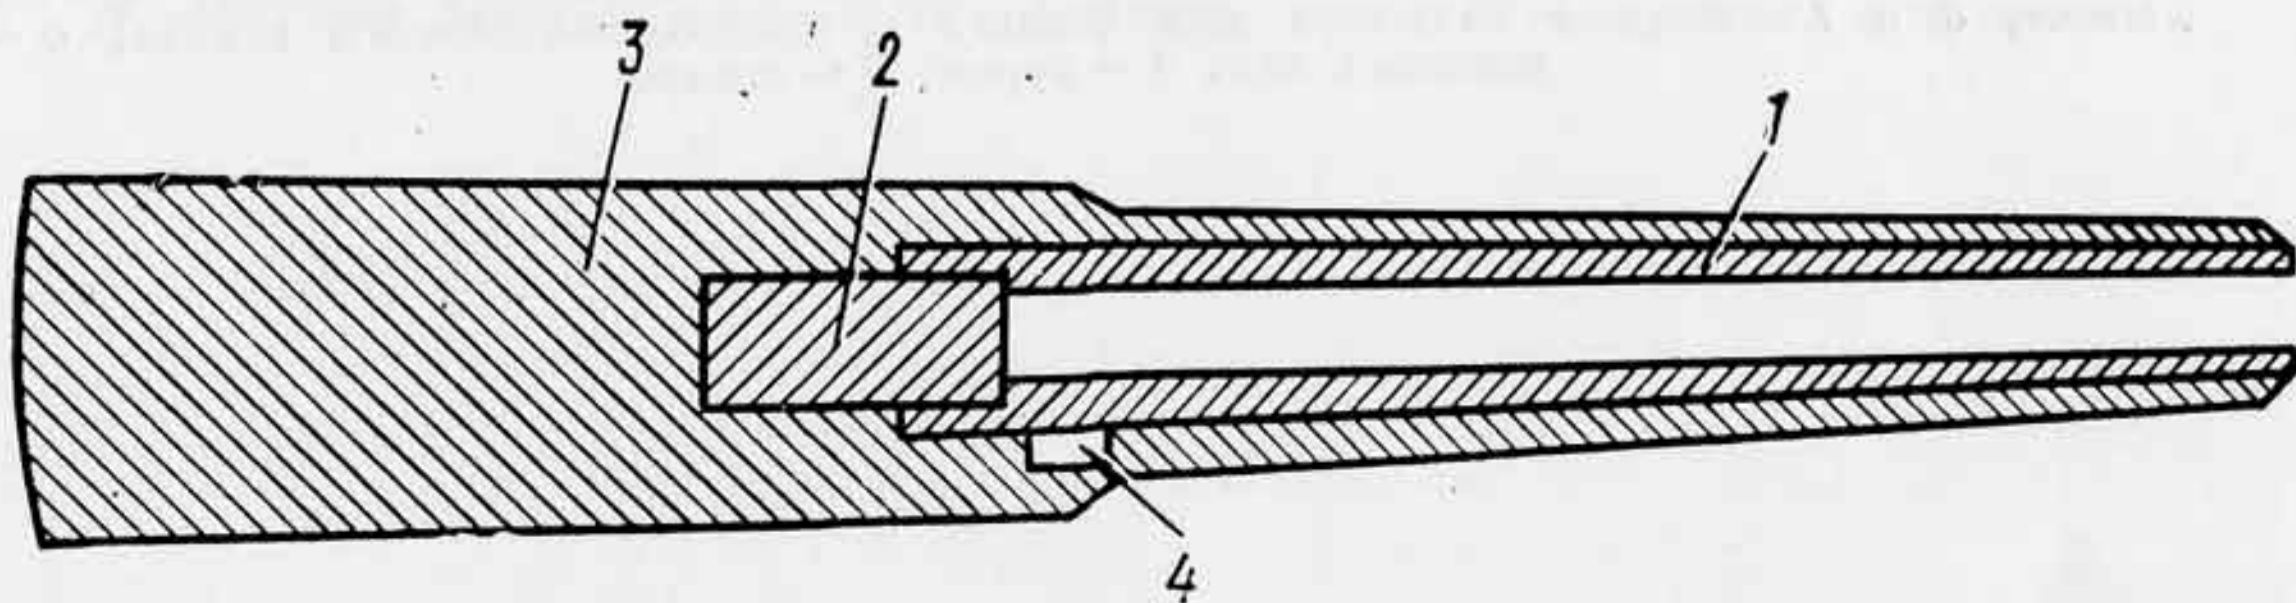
Схематический чертеж ручной пищали середины XV в. (вид сверху):
